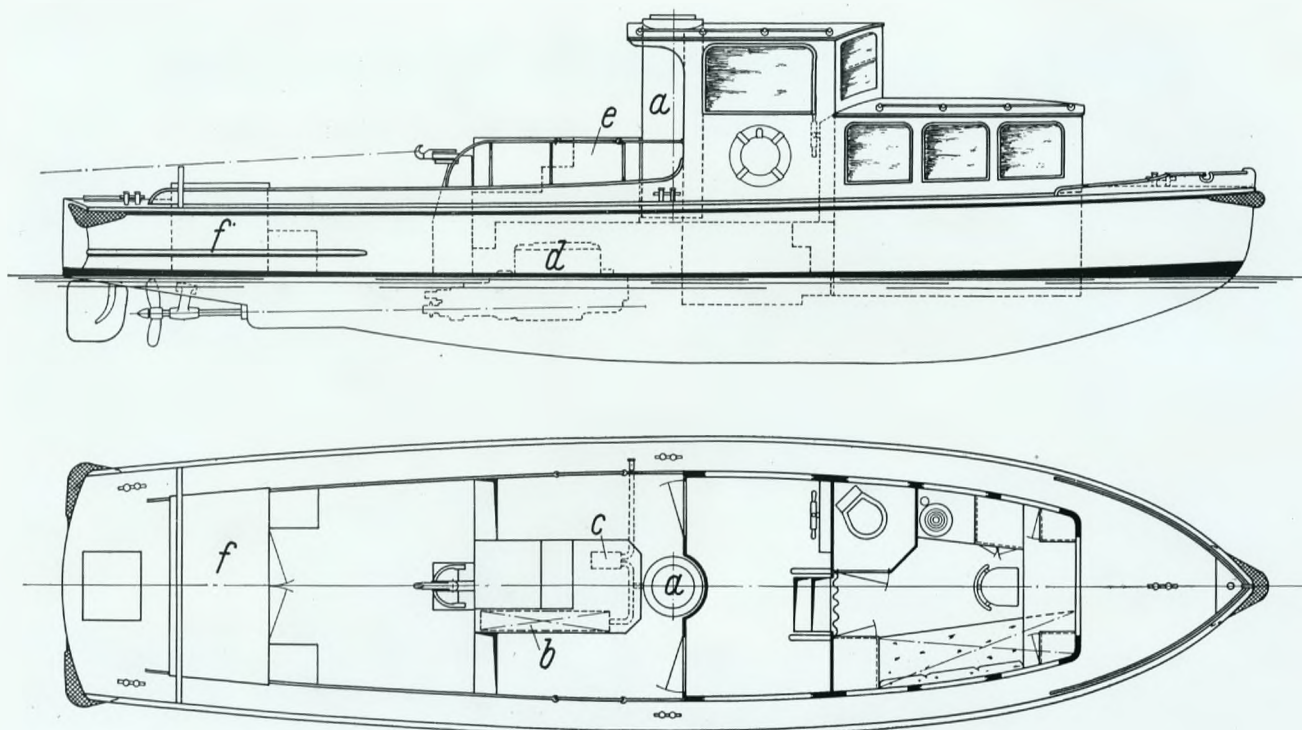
Motoraufsichts- und Schleppboot für Holzgasbetrieb
